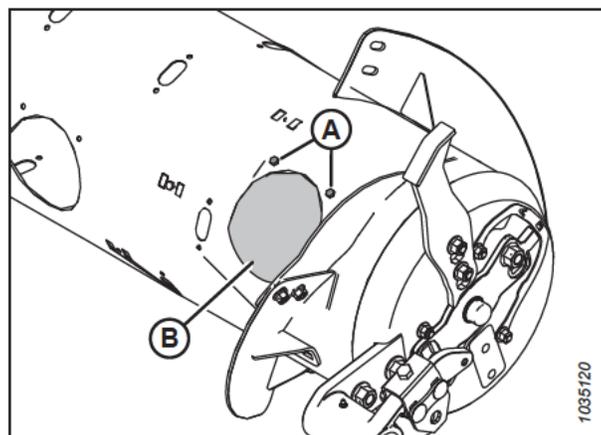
Tampas de acesso do sem fim - Lado direito
